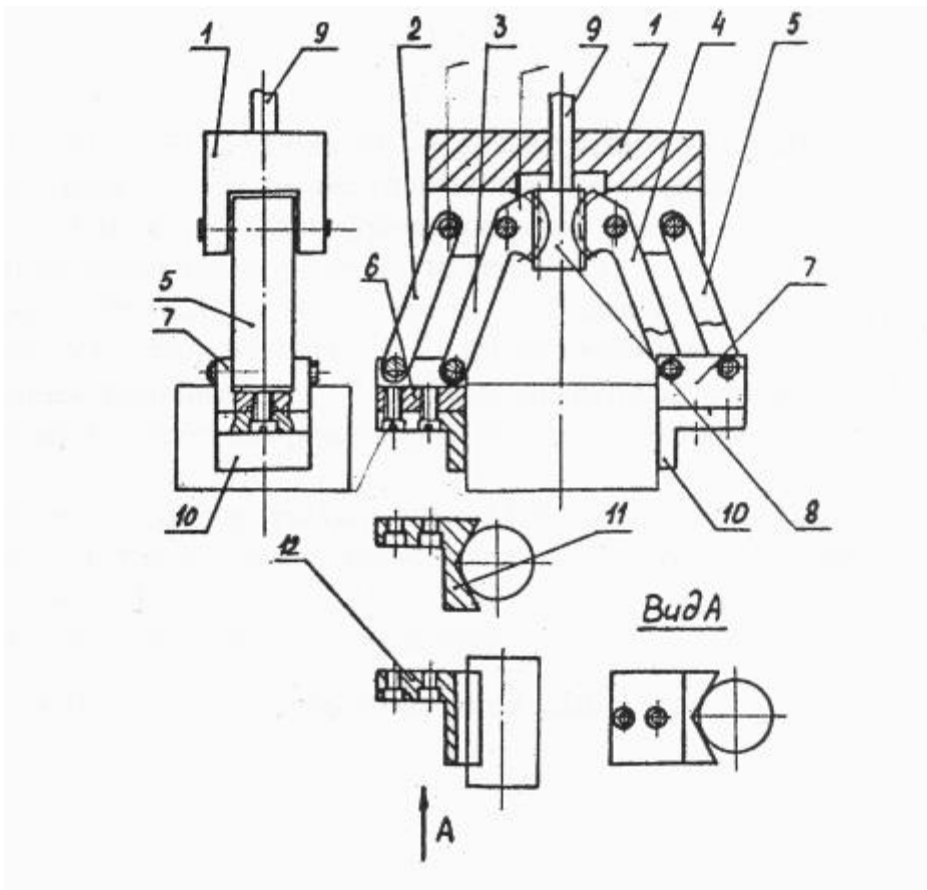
ЗУ с параллельными губками для коробчатых деталей и тел вращения
